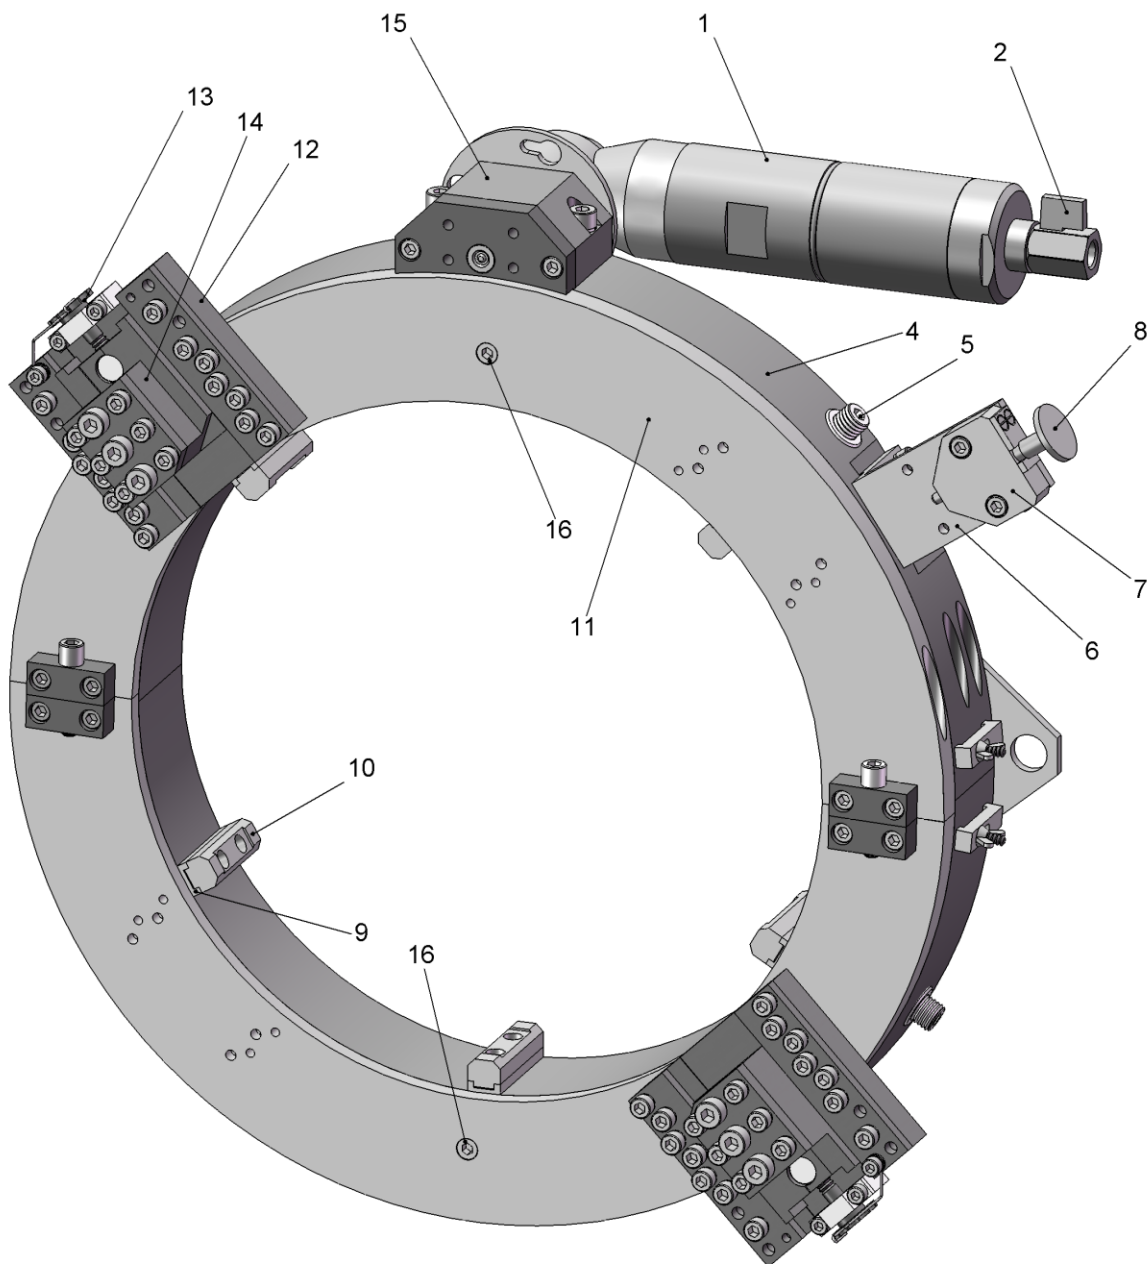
Труборез с отрезными суппортами. Общий вид.
